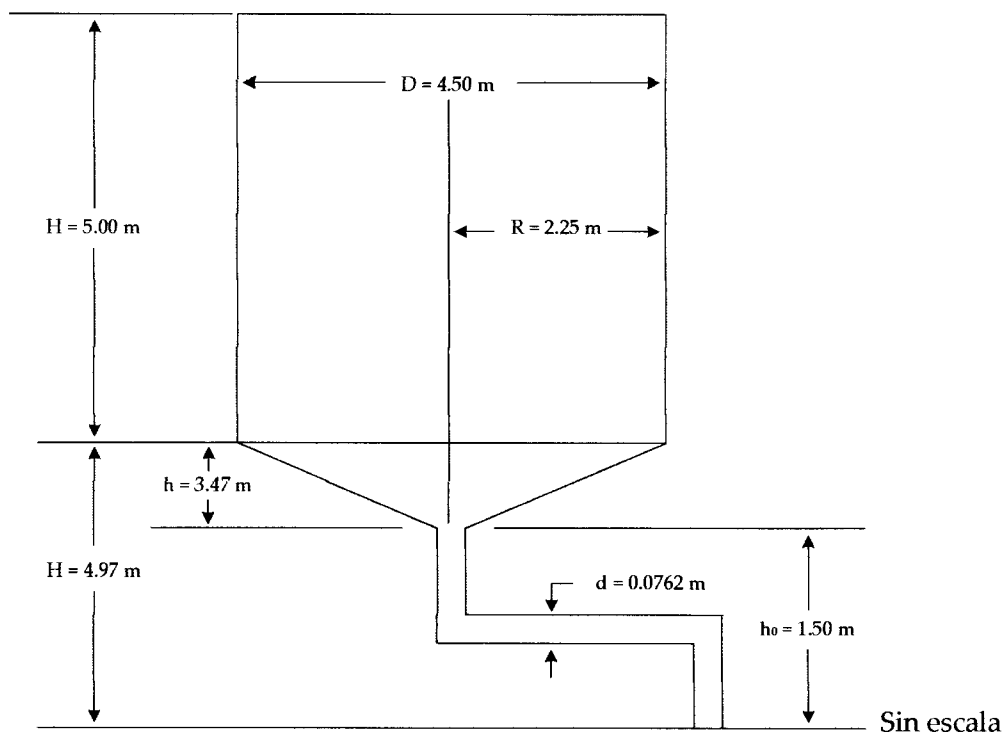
Dimensiones del tanque sedimentador a utilizar en el proceso de reciclado de soda cáustica, en la fabricación de cerveza.
